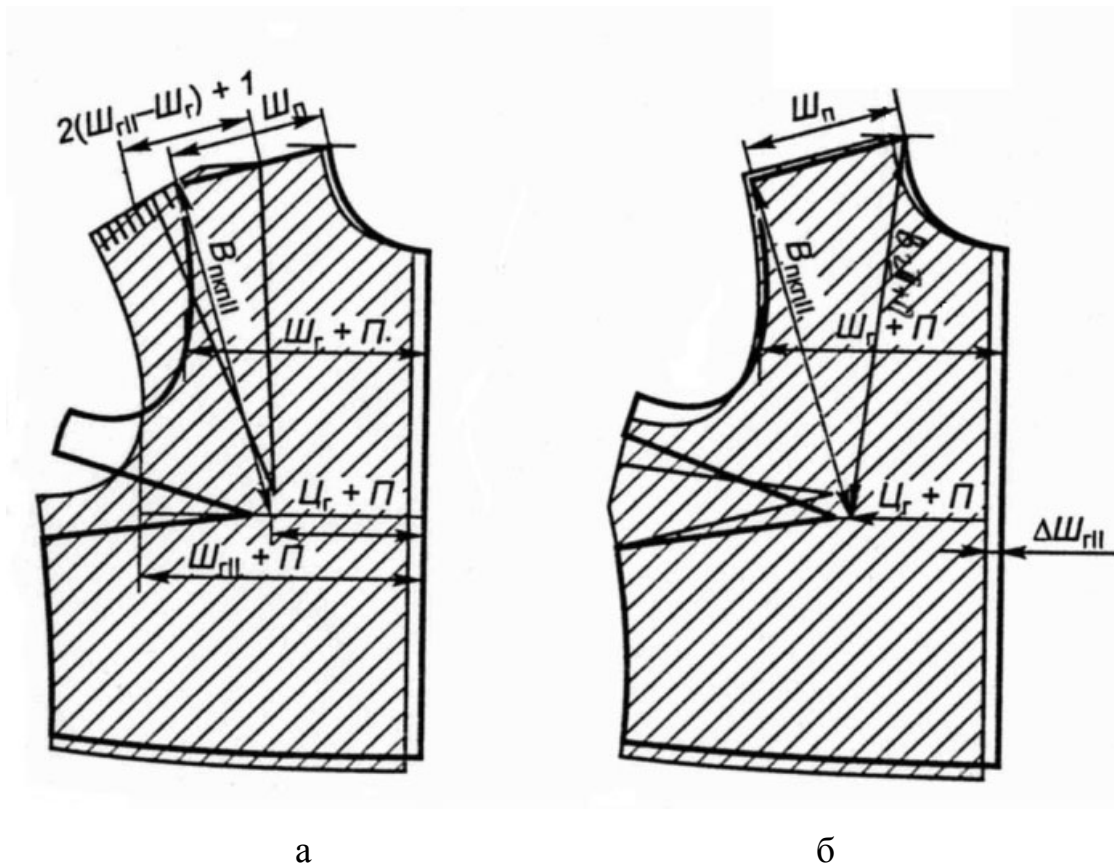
Намелка полочки с вытачкой из бокового среза:
